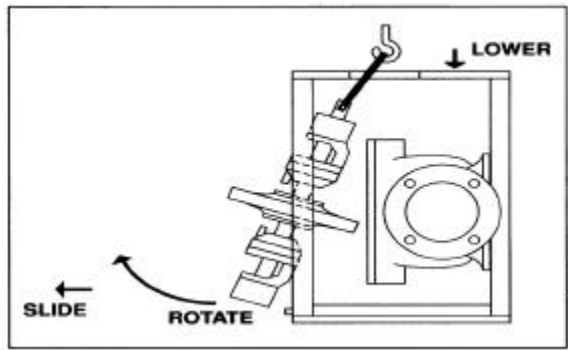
BAJANDO EL ELEMENTO GIRATORIO
